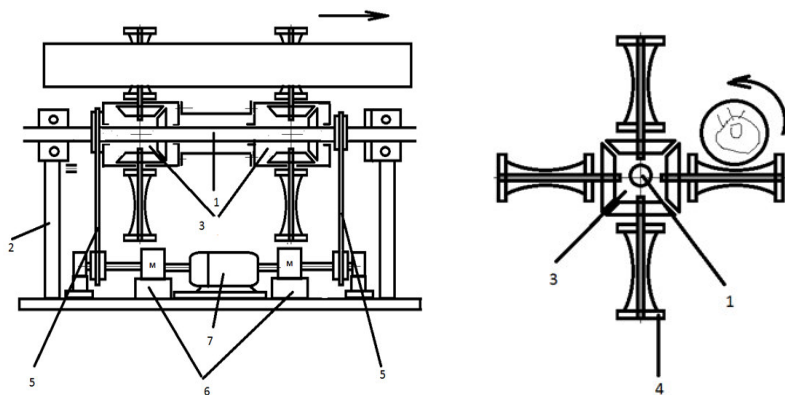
Устройство для сортировки лесоматериала (главный вид):
